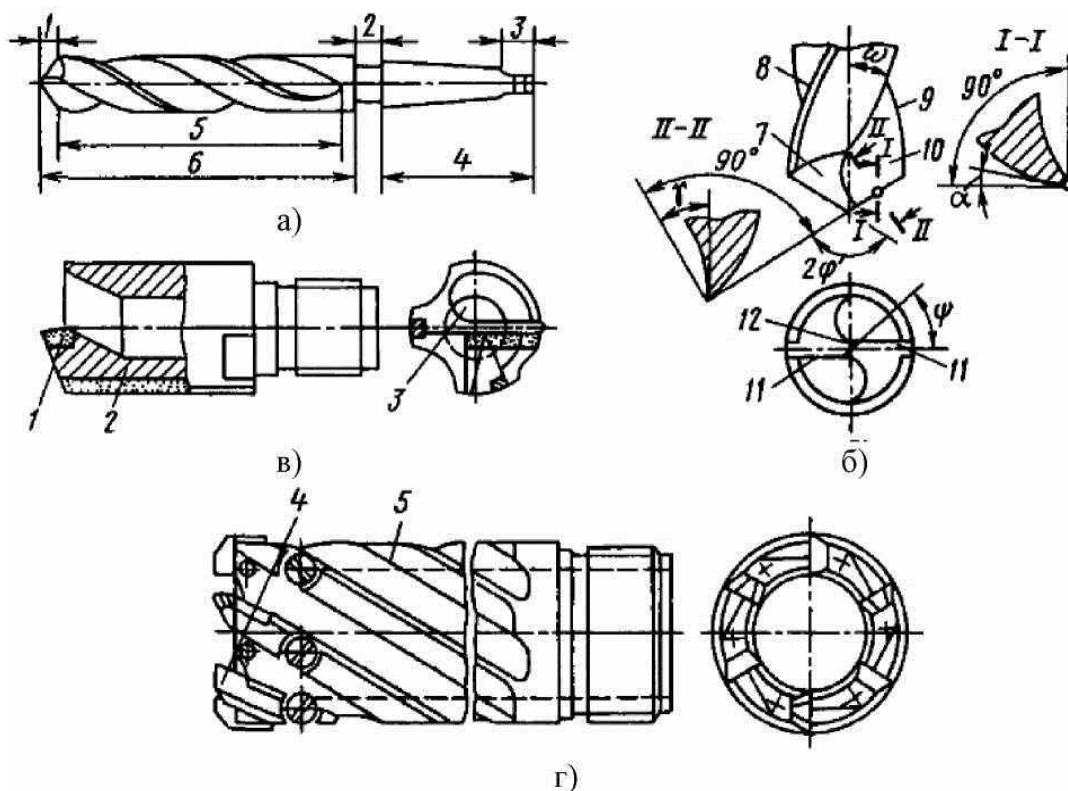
Конструкції свердел: а), б)-частини, елементи та кути спірального свердла; в), г)-спеціальні свердла для глибокого свердлення.
